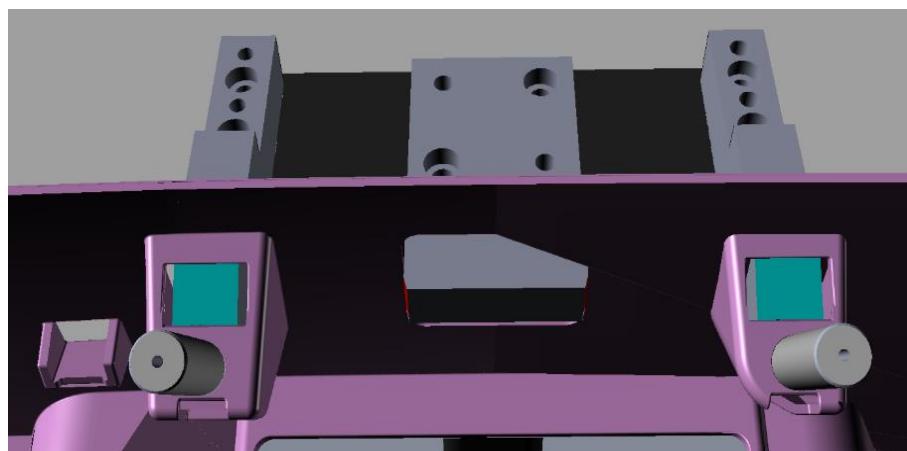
CAD Pieza del posicionador para RPS (Z8-Z9)
